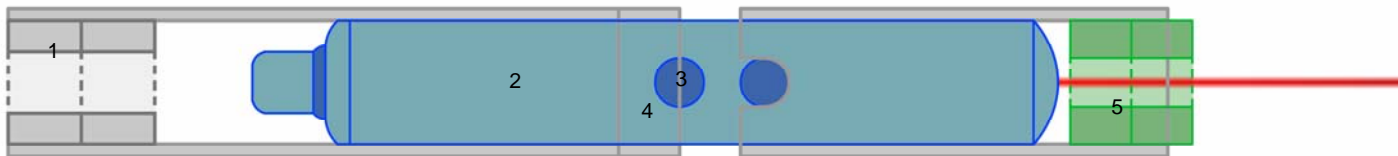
Plan zur Konstruktion des Pendelkopfes, inkl. Nummerierung.
